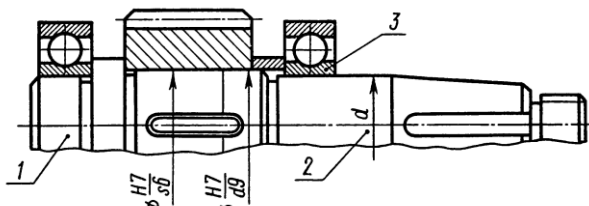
Прямой ступенчатый вал: 1 – шип; 2 – шейка; 3 – подшипник
